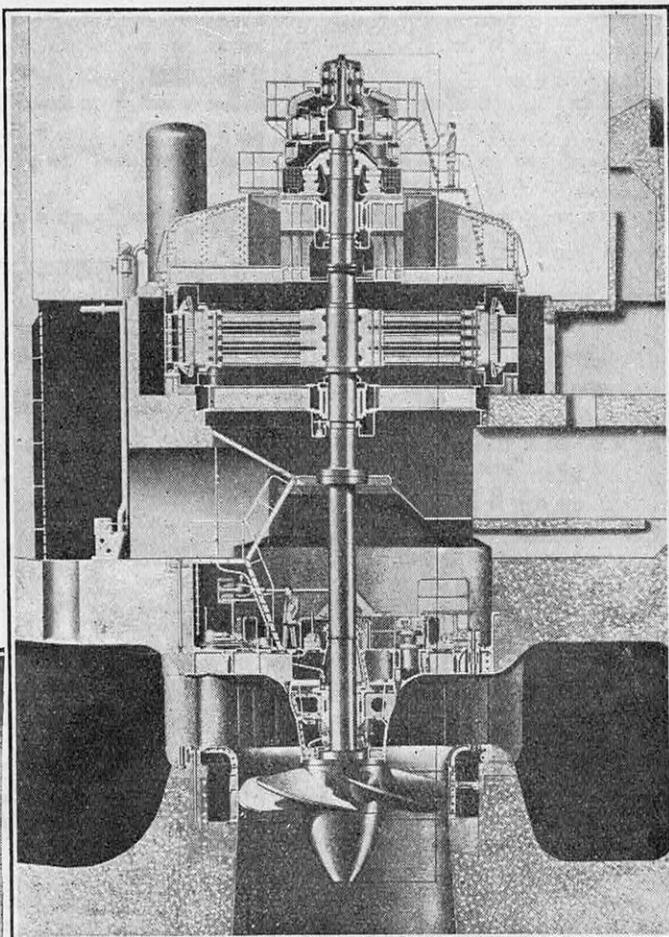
VUE EN COUPE D'UN DES GROUPES TURBOALTERNATEURS DE 36.600 CH DE LA CENTRALE DE KEMBS
